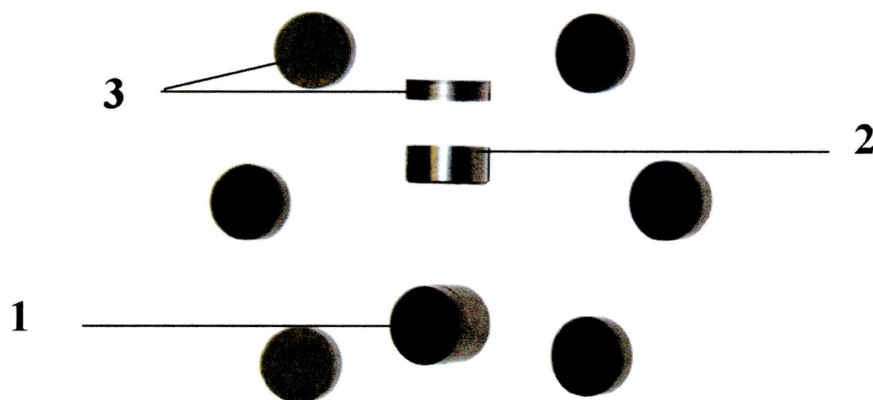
Алмазно-твердосплавні пластини для бурового інструменту: 1, 2, 3 – АТР, твердосплавна підкладка і АТП відповідно.
